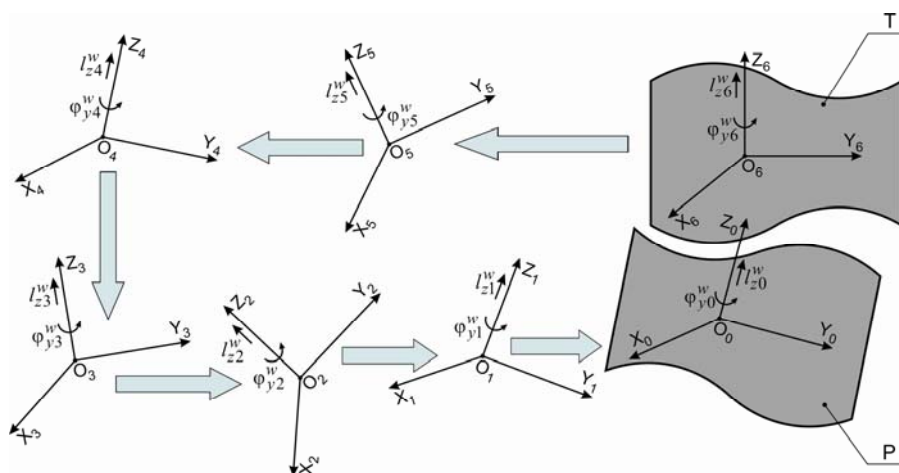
Схема области существования обобщенной кинематической схемы формообразования зубчатых звеньев различных классов, типов и видов (Т – формообразующее зубчатое звено; Р – формообразуемое зубчатое звено).
